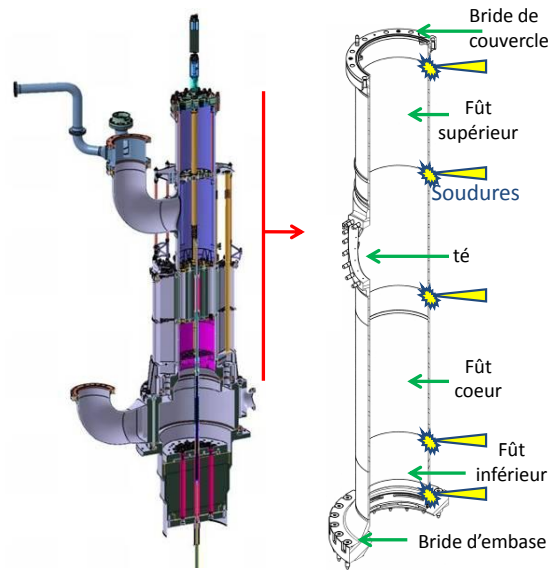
Vue isométrique du caisson et position des soudures (inspiré de [BOU 12]).
